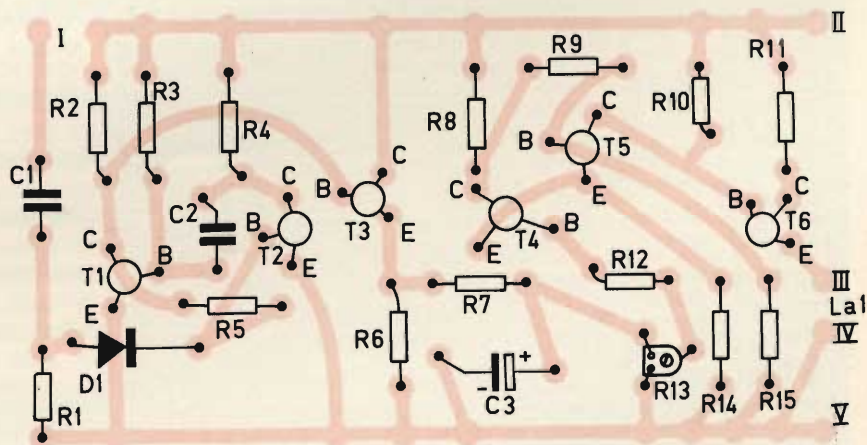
Disegno illustrante la disposizione dei componenti sul circuito stampato.
